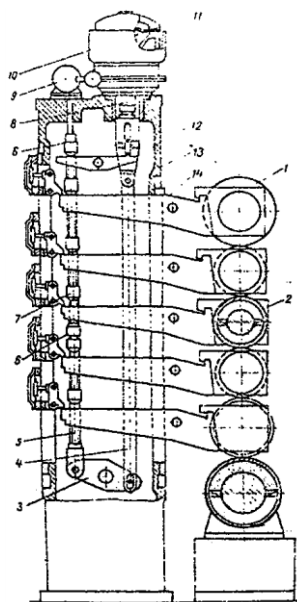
Машинний каландр: 1 – металеві вали; 2 – корпус підшипника; 3 – коромисло вилегчування валів; 4 – сполучні тяги; 5 – тяги підйому і притиску валів; 6 – упори притиску валів; 7 – упори підйому і притиску валів; 8 – гвинти підйому валів; 9 – електродвигун механізму підйому валів; 10 – черв’ячний редуктор підйому валів; 11 – діафрагма притиску валів; 12 – коромисло притиску валів; 13 – станина; 14 – важелі валів
